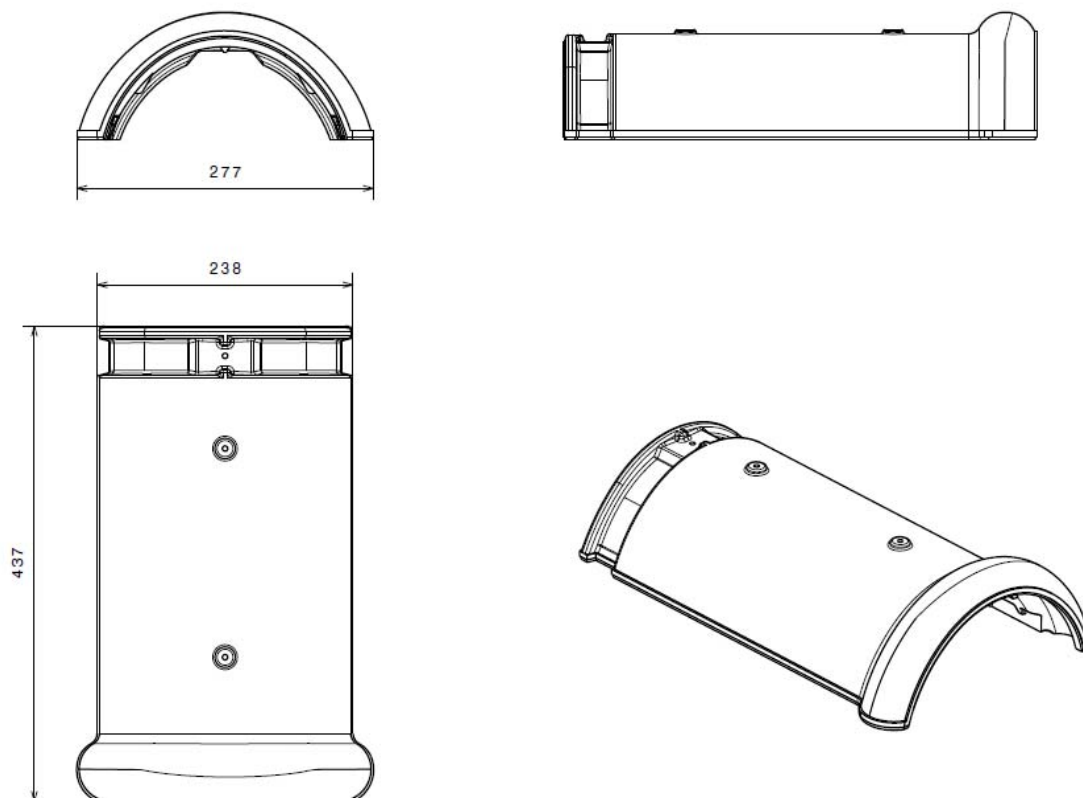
Faîtière ronde ventilée – Section de ventilation de 10 cm²
